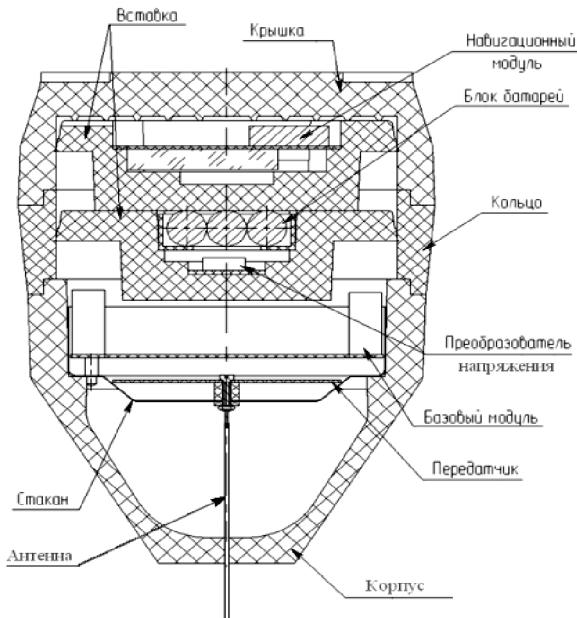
Схема компоновки АРЗ МРЗ-Н1.
